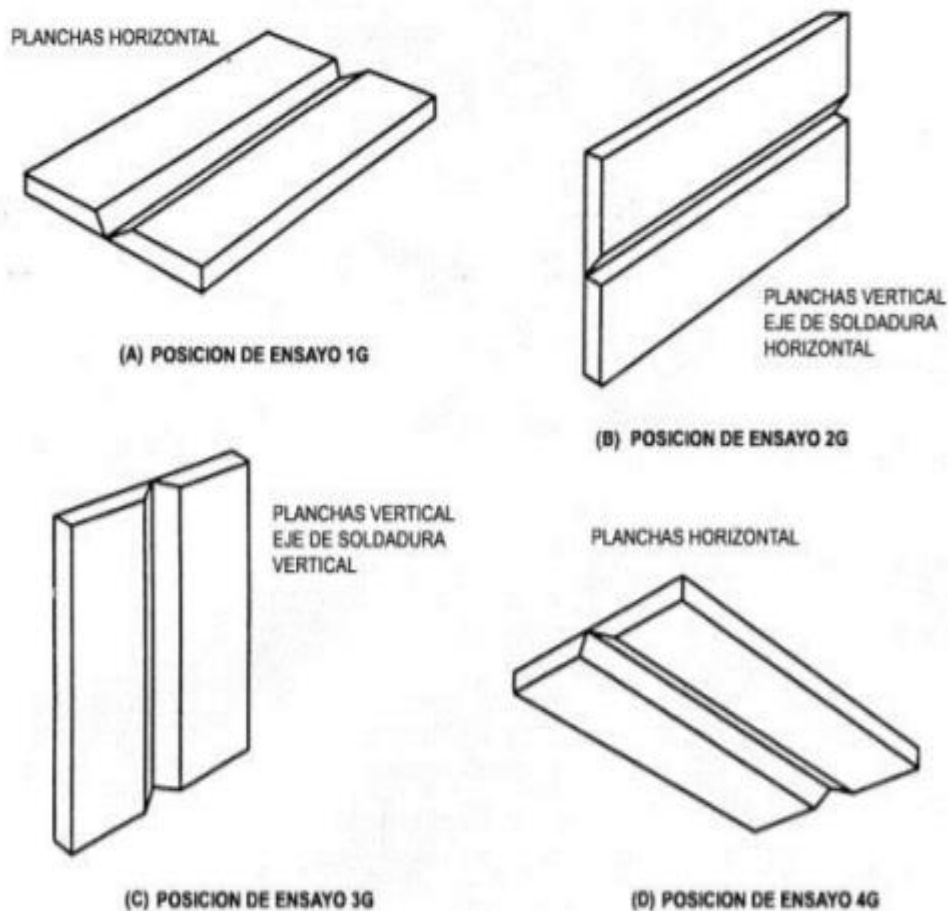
Posiciones de Planchas de Ensayo para Soldadura de Ranura (ver 4.2.4)
